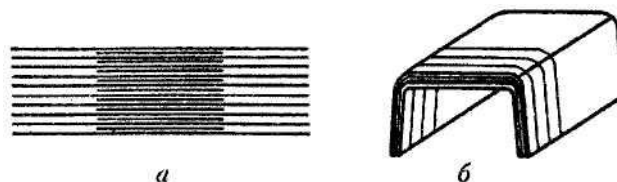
Схема формування пакета при виготовленні багатократної заготовки змінного перерізу:
